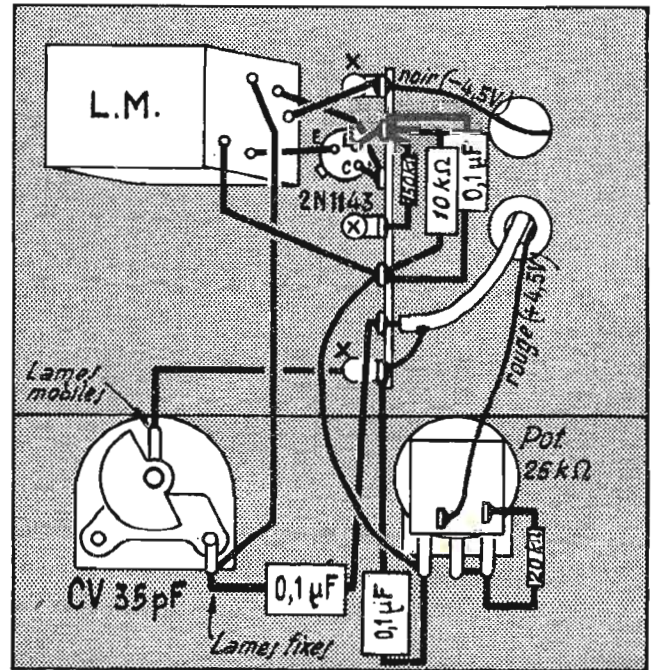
b. — Vue de dessous, avec face avant rabattue
